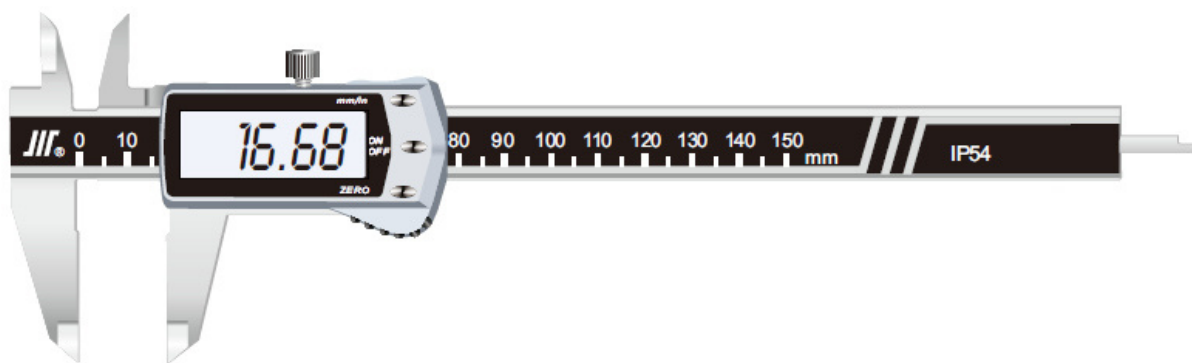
Общий вид штангенциркулей модели ШЦЦ-I
